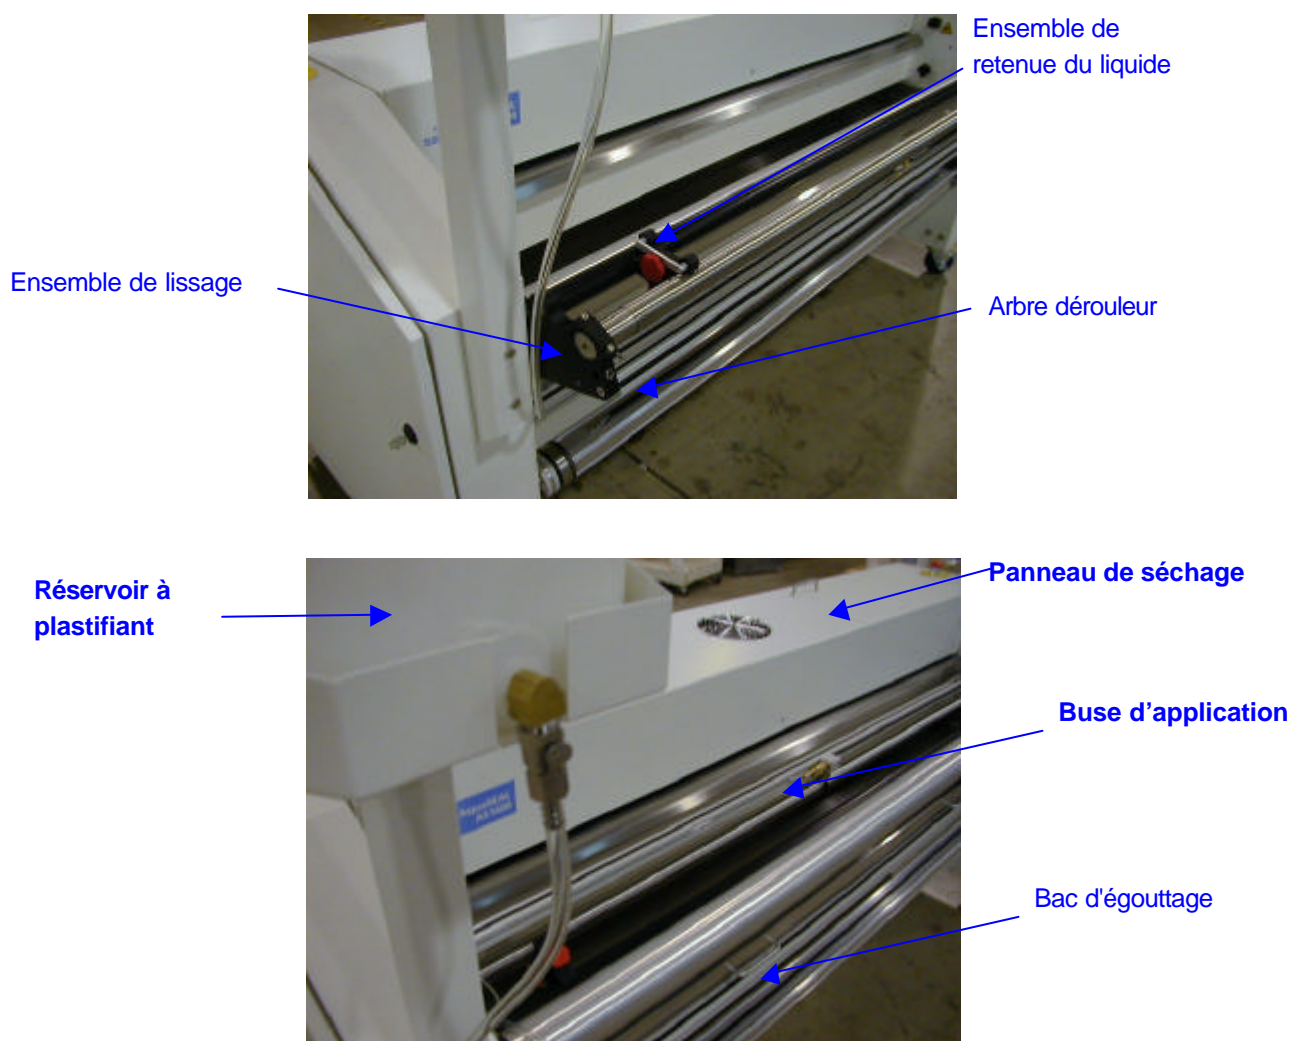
AquaSEAL™ AS-1600* Vues frontales
